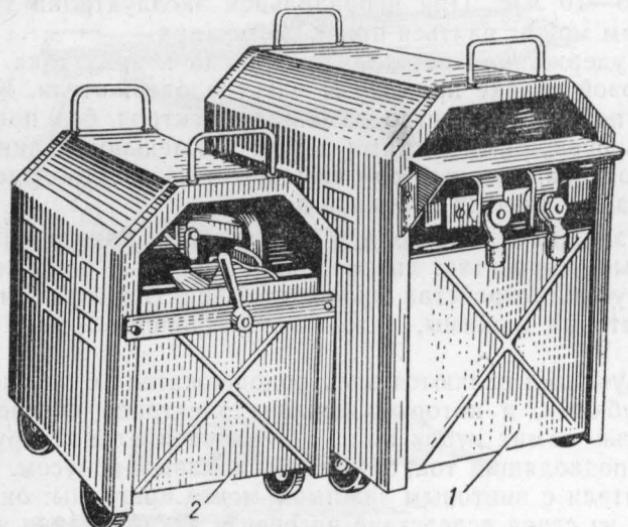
Сварочный трансформатор СТЭ-34
